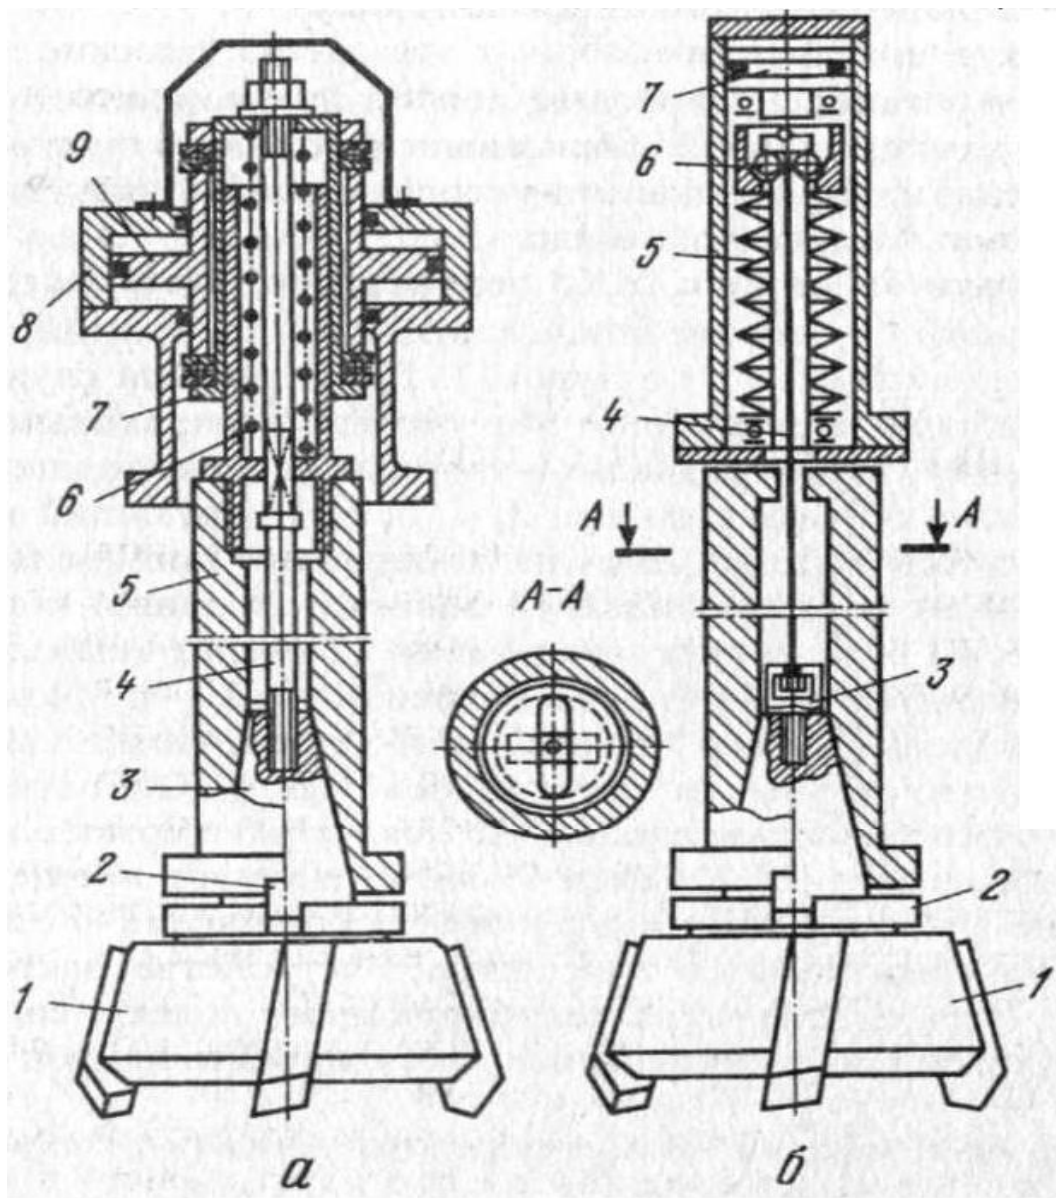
Приспособления для механизированного закрепления фрез в шпинделе: а – с наворачиванием хвостовика на тягу, б – с поворотом хвостовика на 90° .
